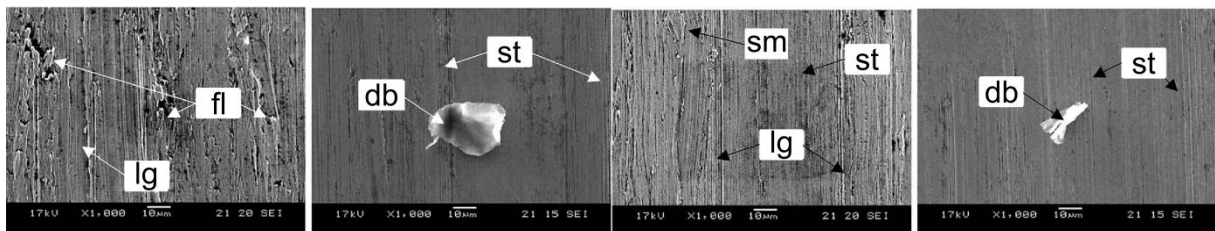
Images MEB de défauts de surface à l'échelle macroscopique - Inconel 718 usiné avec un outil en carbure -  $V_c = 60$  m/min,  $f = 0.1$  mm/tr,  $a_p = 0.5$  mm (Arunachalam et al., 2004b) : lg = Long groove (rainures), fl = flash (fractures, éclats), db = debris (débris), st = streaks (rayures), sm = smearing (beurrage).
